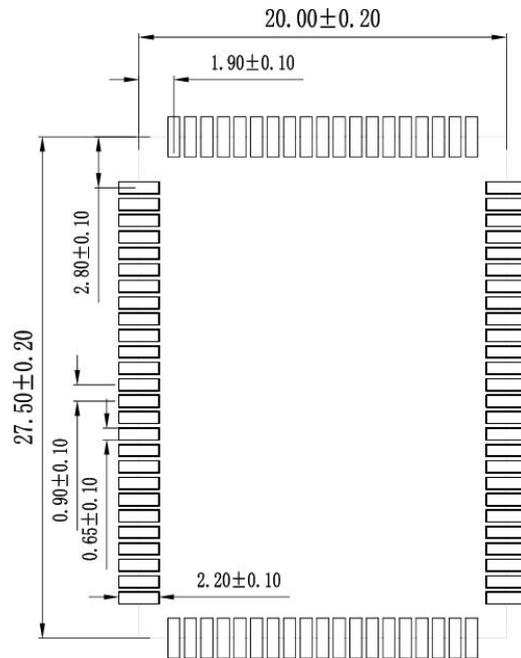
推荐 PCB 封装尺寸 (TOP 视图)
